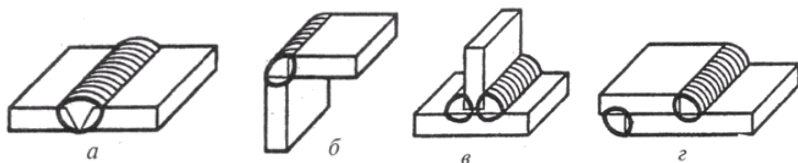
Типы сварочных соединений: стыковые (а), угловые (б), тавровые (в) и нахлесточные (г)
